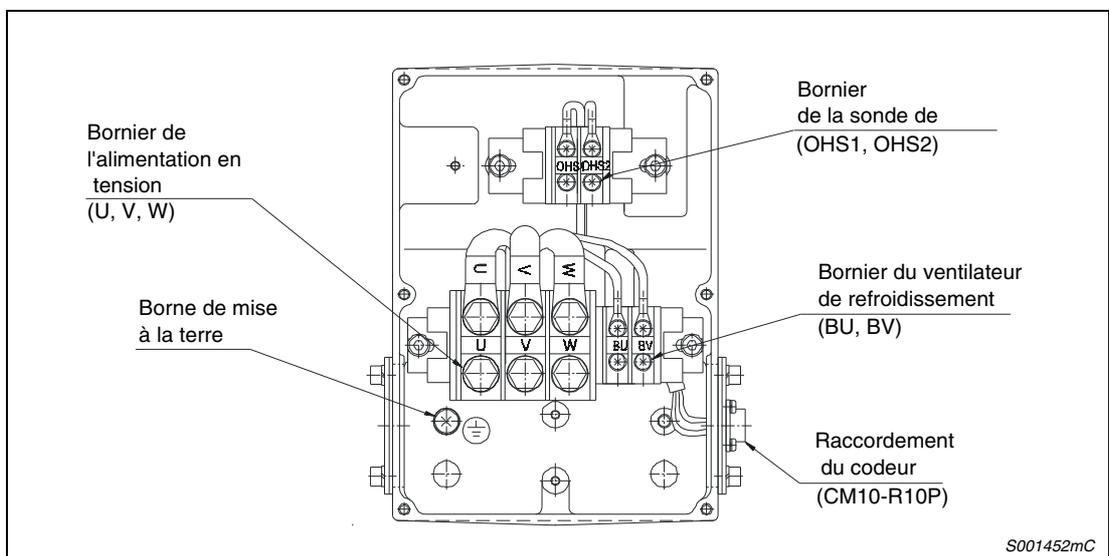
Bornier des moteurs HA-LP11K2(4)(B)
